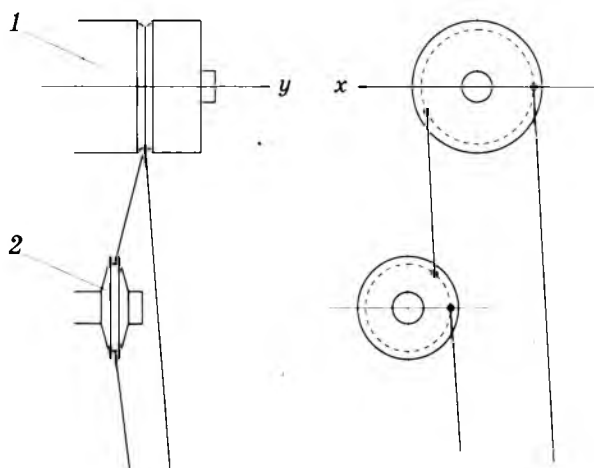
Схема размещения шкивов цилиндрического барабана:
